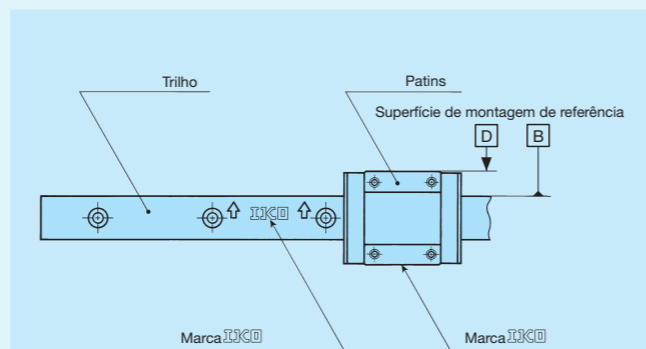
Superfície de montagem de referência de produtos diferentes de LWL1 (Y) e LWLF2
